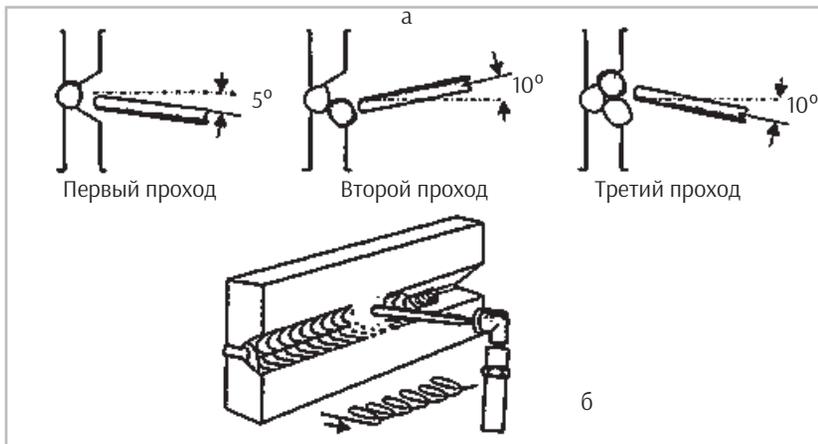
Положение электрода при сварке стыкового соединения со скосом кромок в горизонтальном положении: а — сварка с поперечными колебаниями электрода; б — пример поперечных движений торца электрода
